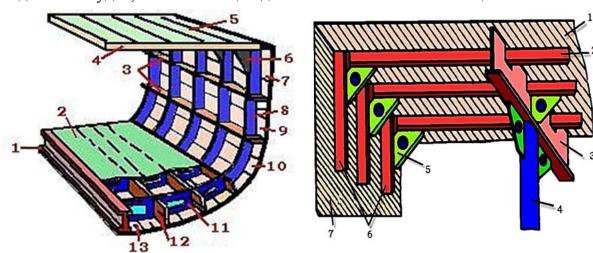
Смешанный набор судна 1-киль; 2-настила второго дна; 3-бортовые стрингеры; 4-бимс; 5-палубный стрингер; 6-кница; 7-ширстрек; 8-шпангоут; 9-бортовой пояс; 10-скуловой пояс; 11-флор; 12-днищевой стрингер; 13-килевой пояс
